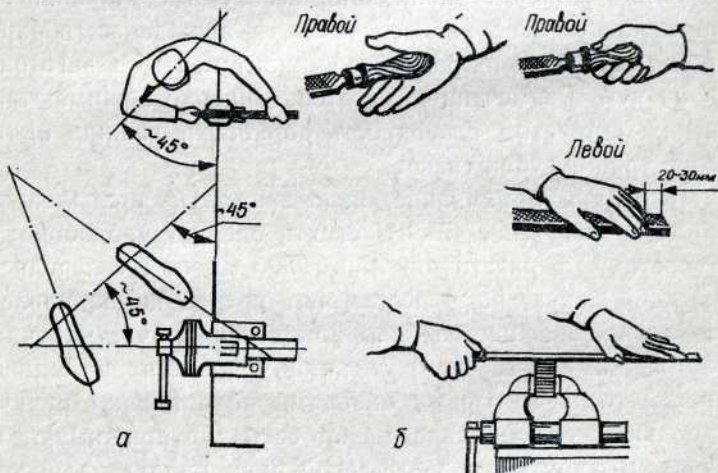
Опиливание заготовок: а — рабочая поза; б — хватка инструмента.
